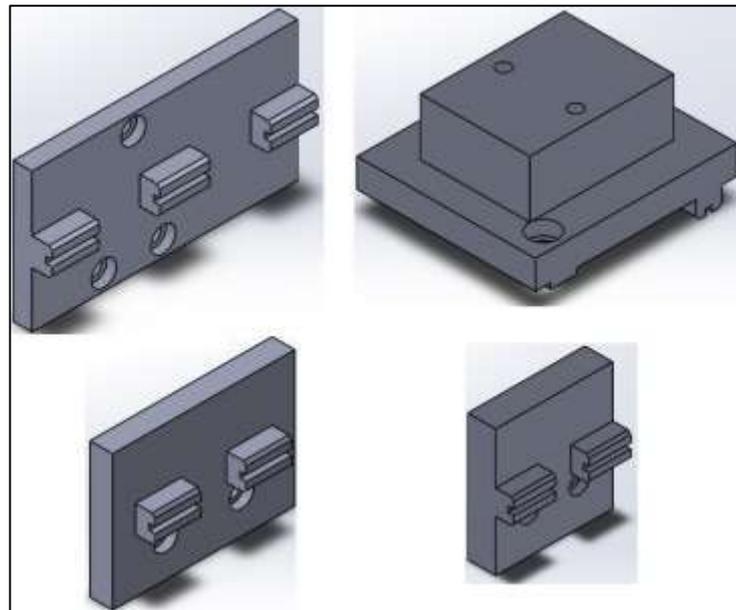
Diseño de soportes en SOLIDWORKS.
